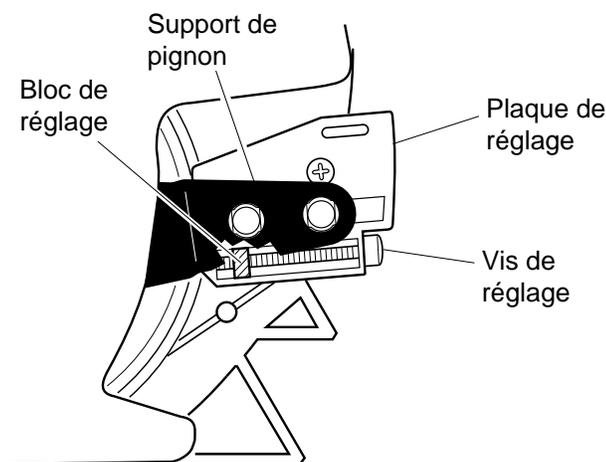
Emplacement des pièces pour l'assemblage de la lame-guide
